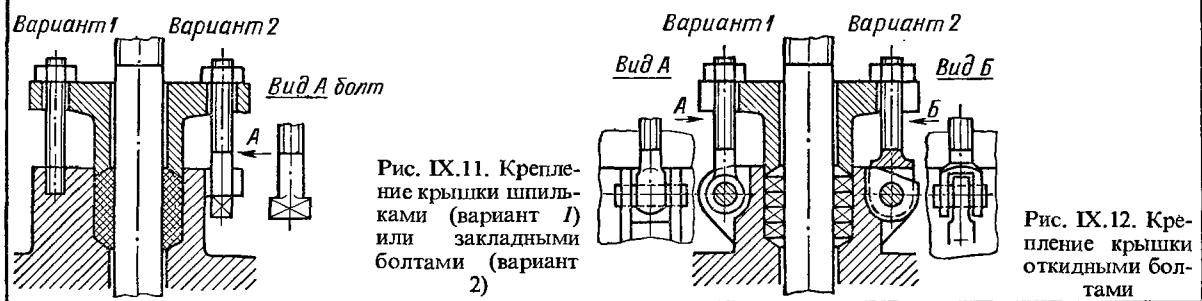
Крепление крышки шпильками (вариант 1) или закладными болтами (вариант 2)
